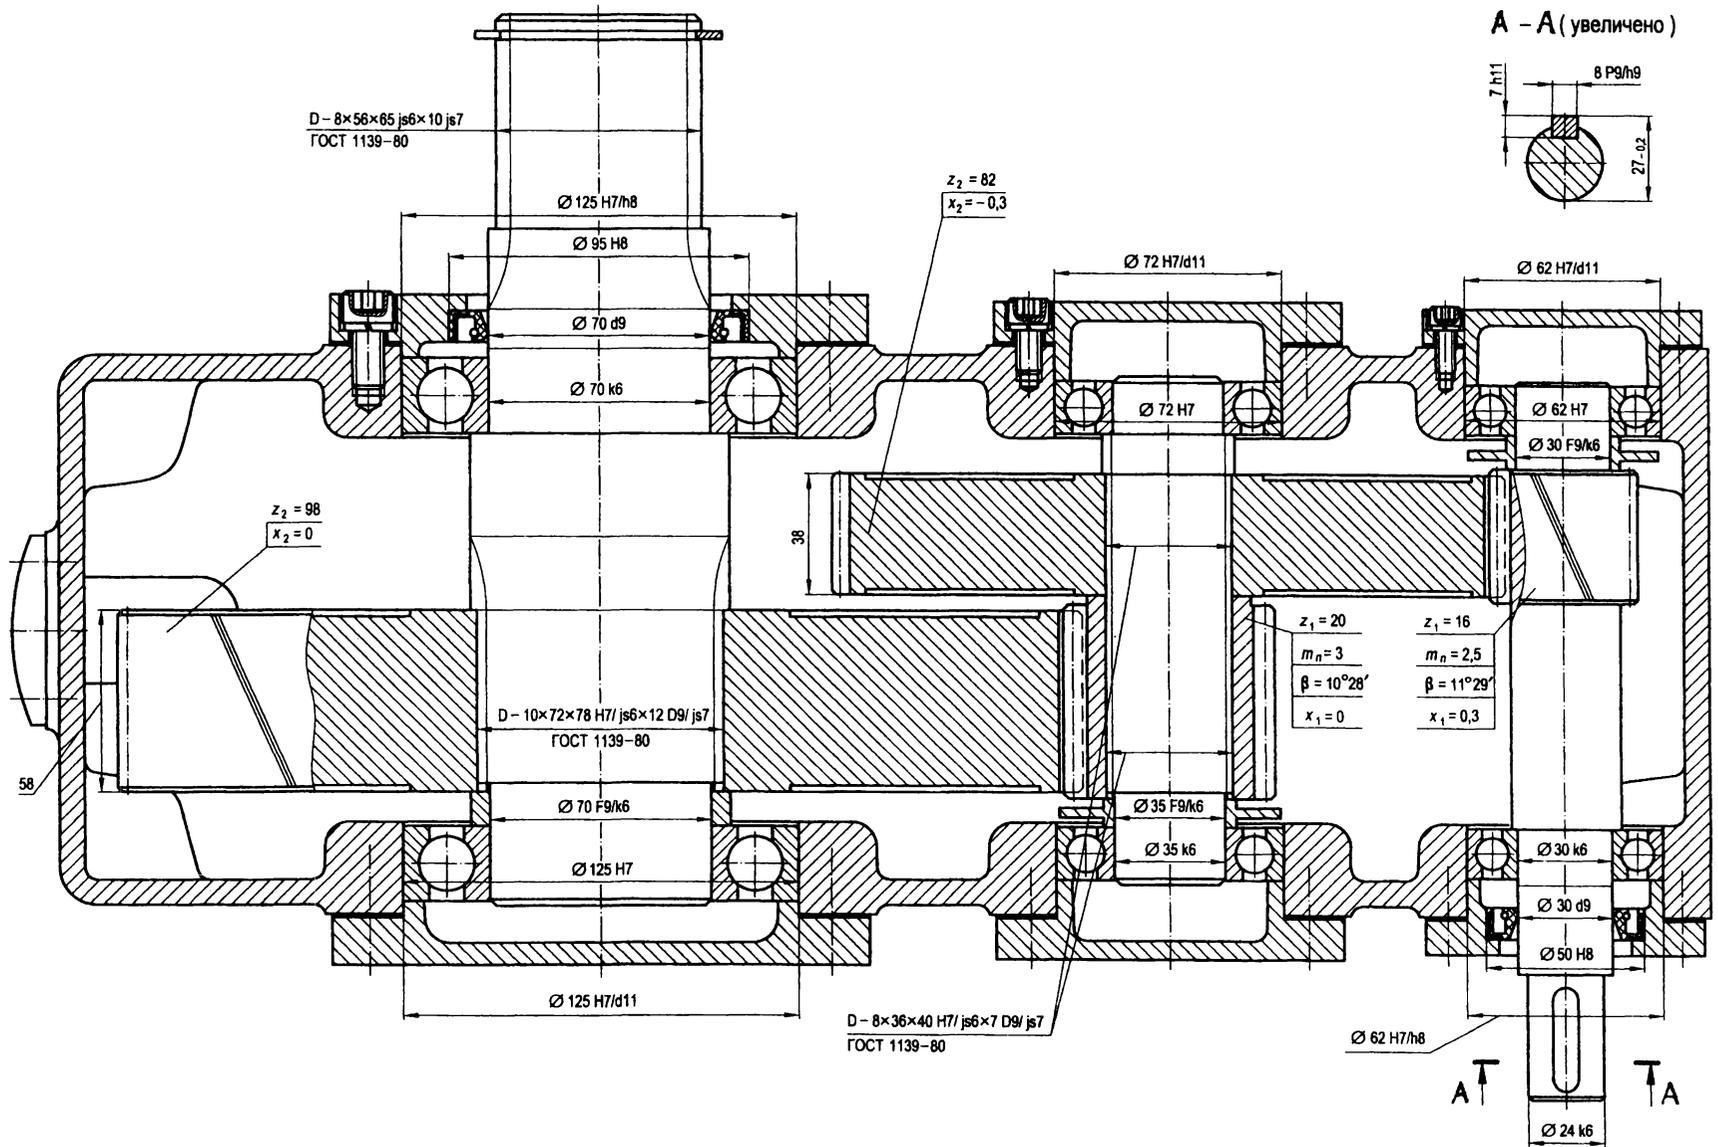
Редуктор двухступенчатый цилиндрический горизонтальный, выполненный по развернутой схеме, без разъема корпуса по осям валов
